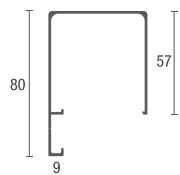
DETAIL ZÁKLADNY (SPODNÍHO PROFILU)
